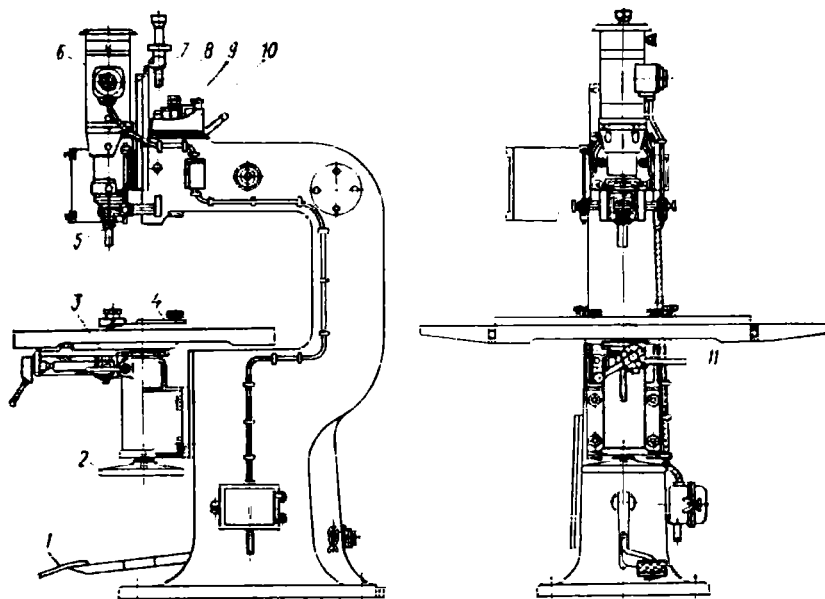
Схема фрезерного копировального станка ВФК-2:
